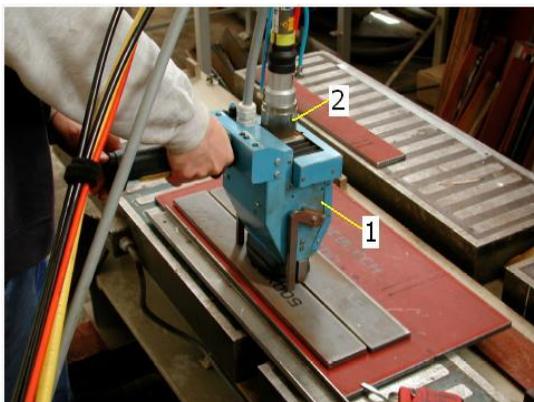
Ручная установка для лазерной гибридной сварки коротких швов.
